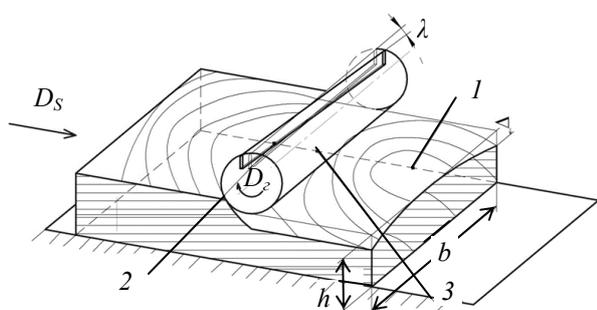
Процесс получения профильной поверхности фрезами с изменяемым осевым углом:
